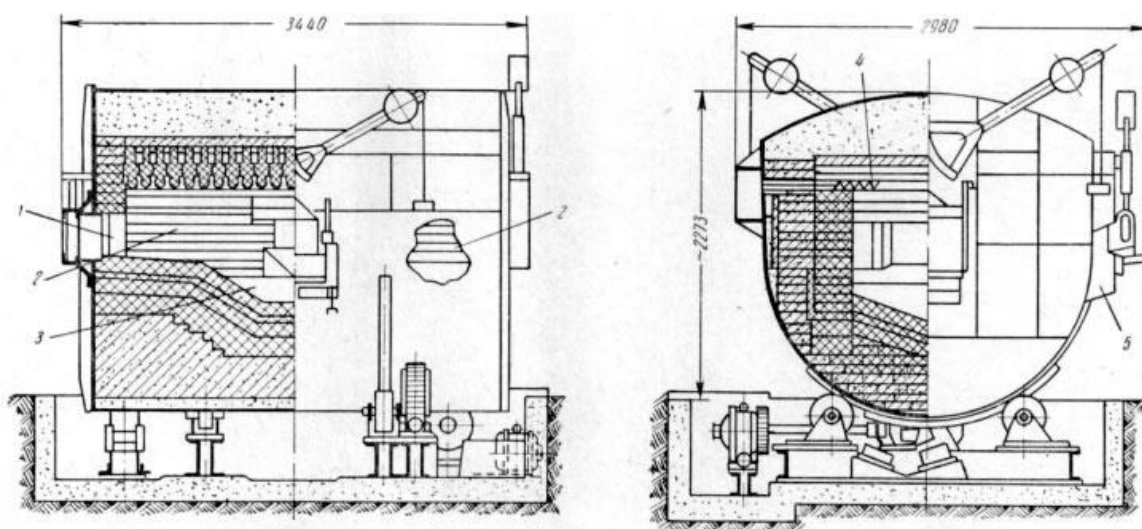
Схема печи сопротивления для плавки алюминиевых сплавов, поворотного типа, САН-36: 1 – загрузочное окно; 2 – рабочее пространство; 3 – ванна жидкого металла; 4 – электронагревательные элементы; 5 – сливной носок
